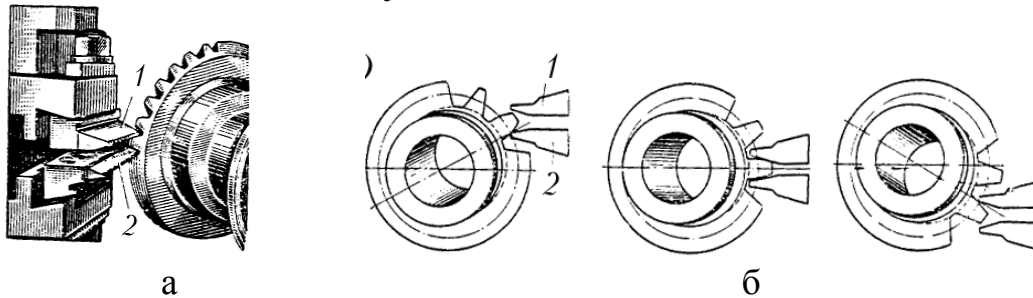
Нарізування конічного зубчастого колеса на зубостругальному верстаті: а – встановлення різців; б – схема обкочування; 1 і 2 – різці.
